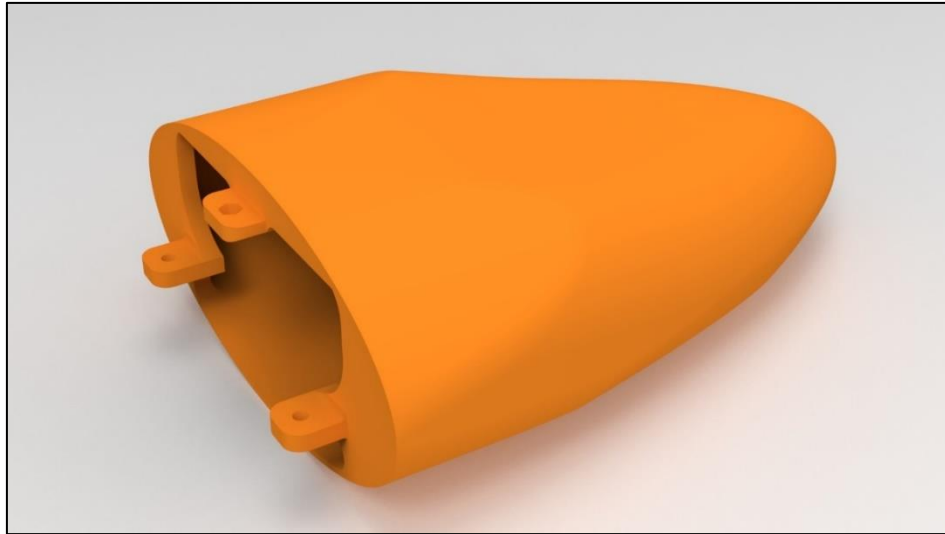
Punta del fuselaje - vista isométrica [Autores].
